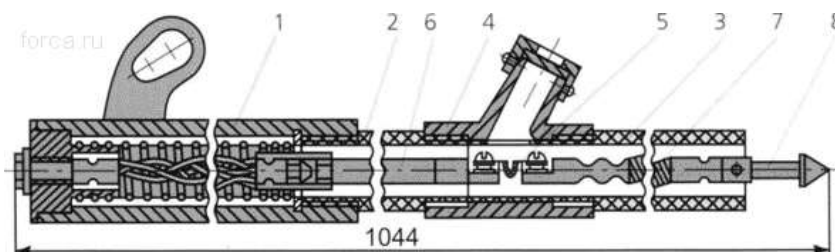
Патрон газогенеруючого запобіжника ПСН – 35: 1 - корпус, 2-3 - вінілпластові трубки, 4 - сталевий патрубок; 5 - плавка вставка; 6 - струмоведучий стержень; 7 - гнучкий провідник, 8 - наконечник.
